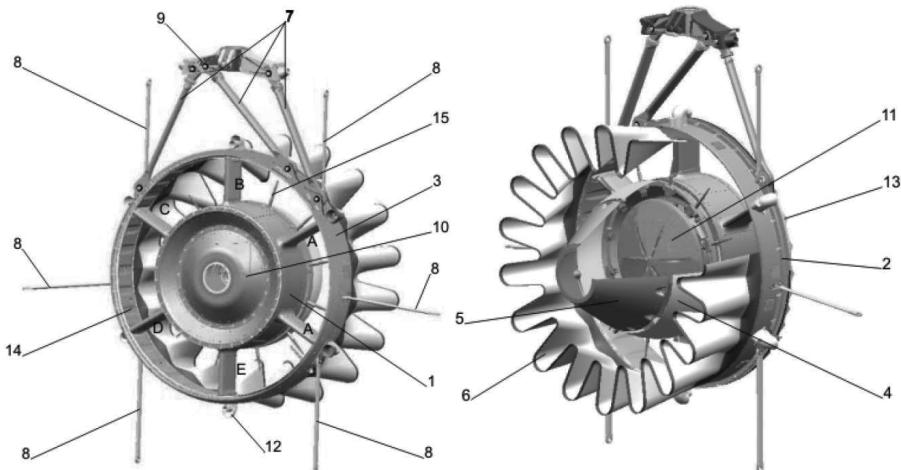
Конструкция задней опоры двигателя ПС-90А:
